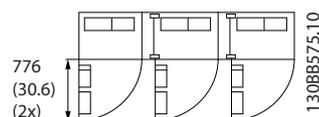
Пространство перед корпусом IP21/IP54, типоразмер F11
